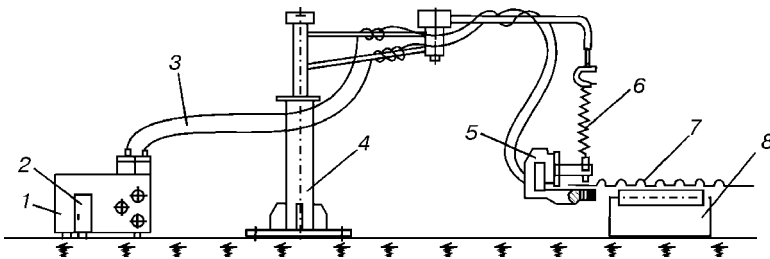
Схема специализированной установки для пробивки отверстий: 1 — гидростанция; 2 — шкаф электрический; 3 — шланг высокого давления; 4 — консоль поворотная; 5 — головка-пресс; 6 — подвеска пружинная; 7 — лист обшивки; 8 — рольганг
